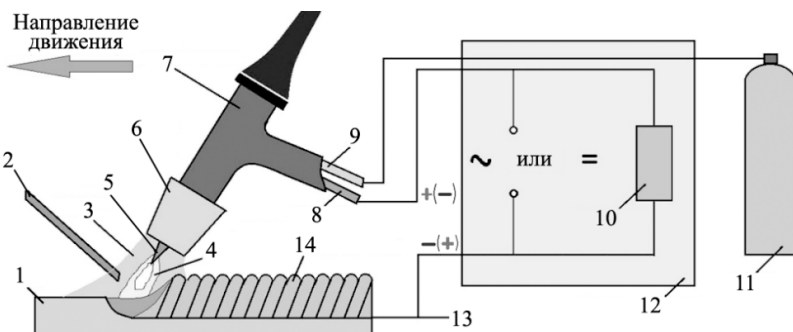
Схема аргонодуговой сварки неплавящимся электродом:
